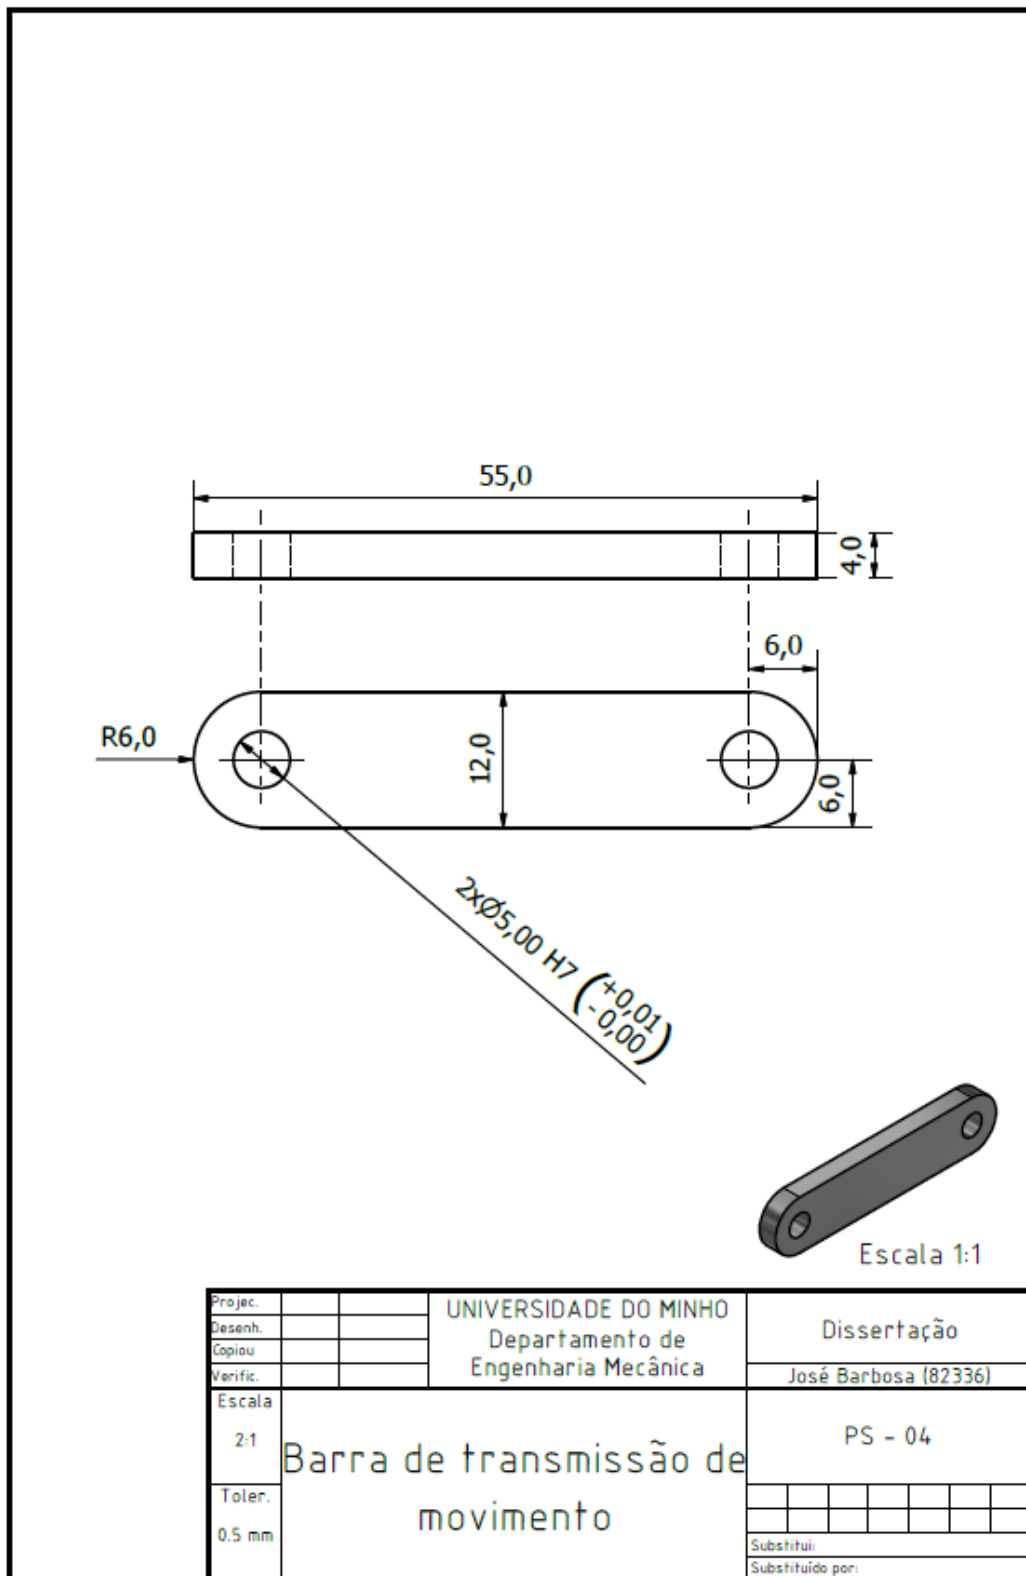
Figura Anexo III-29 – Desenho técnico da barra de transmissão de movimento.
